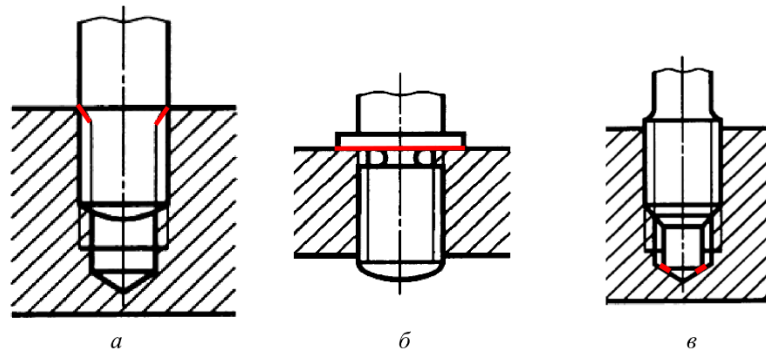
Додаткові конструктивні елементи заклинювання різьби.
